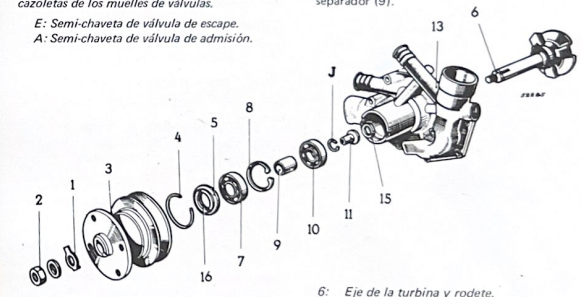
Despiece completo de la bomba de agua de un motor tipo 801.
